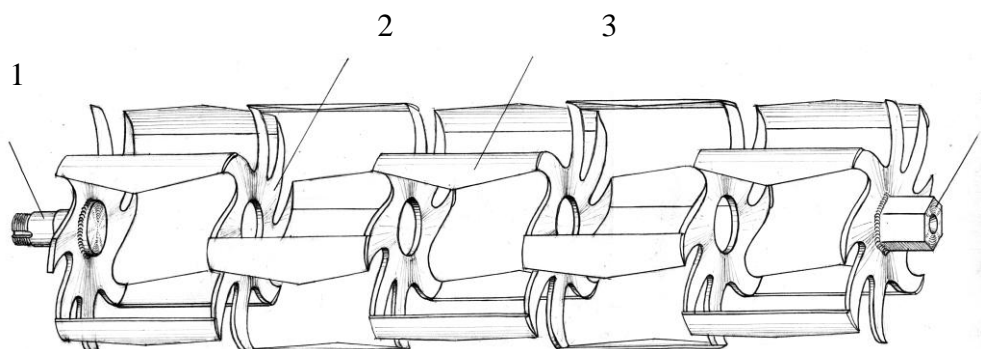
Фрезерный барабан: 1 - цапфа; 2 - дисковая фреза; 3 - режущий нож
